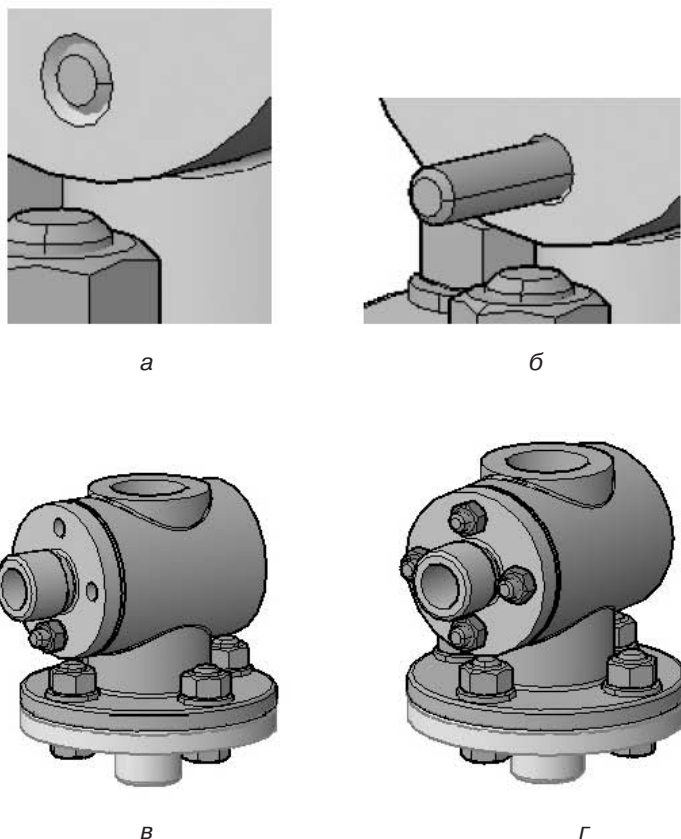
Вставка шпилек, шайб и гаек для крепления бокового фланца: *а* — вставка шпильки в корпус; *б* — смещение шпильки; *в* — вставка шайбы и гайки; *г* — построение массива
